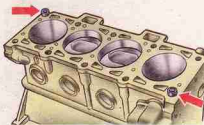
Втулки для центрирования головки на блоке цилиндров
